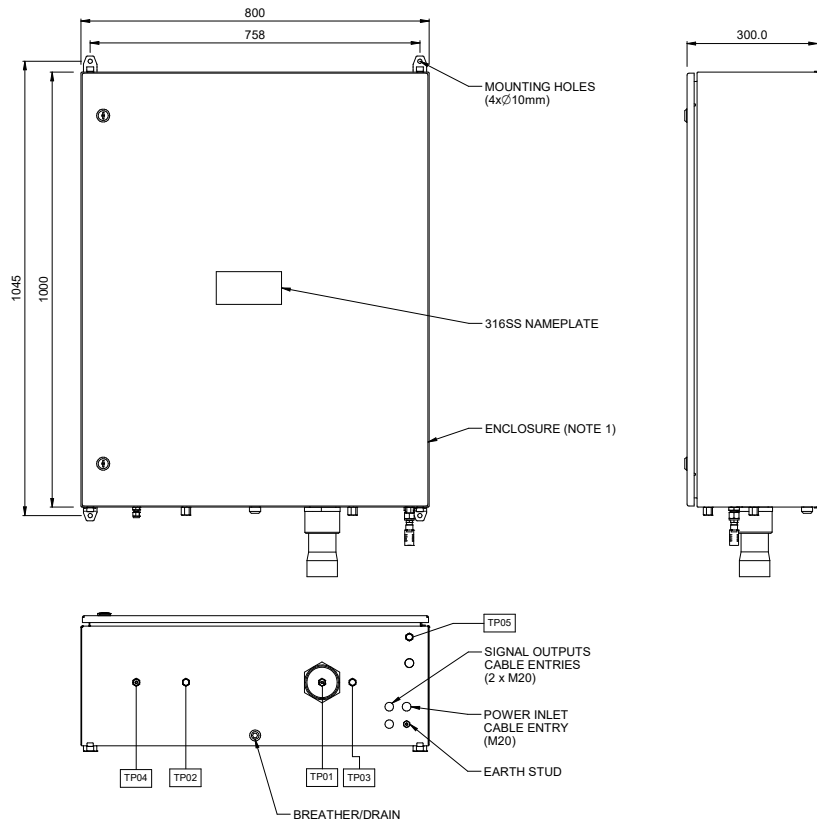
Maßzeichnung – Gehäuse für Außenmontage
